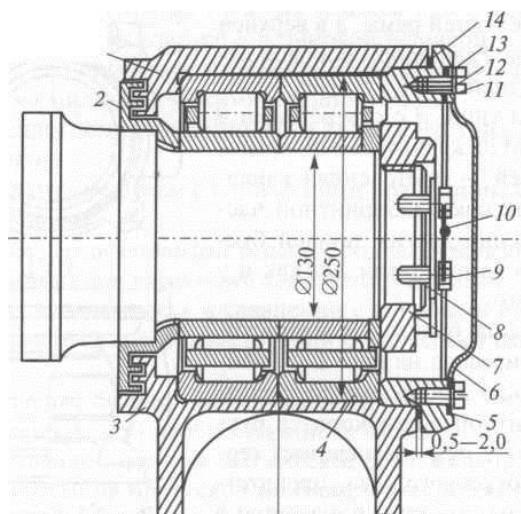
Букса пассажирского вагона с двумя цилиндрическими подшипниками с торцевым креплением гайкой
